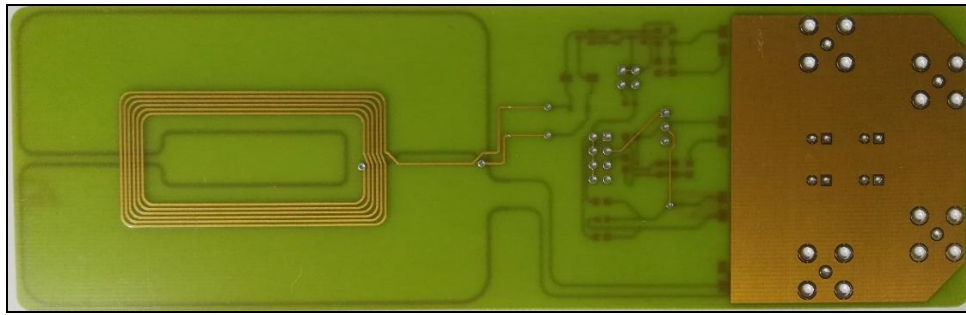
PCB PICC de Referencia N° 6 – Capa BOTTOM
